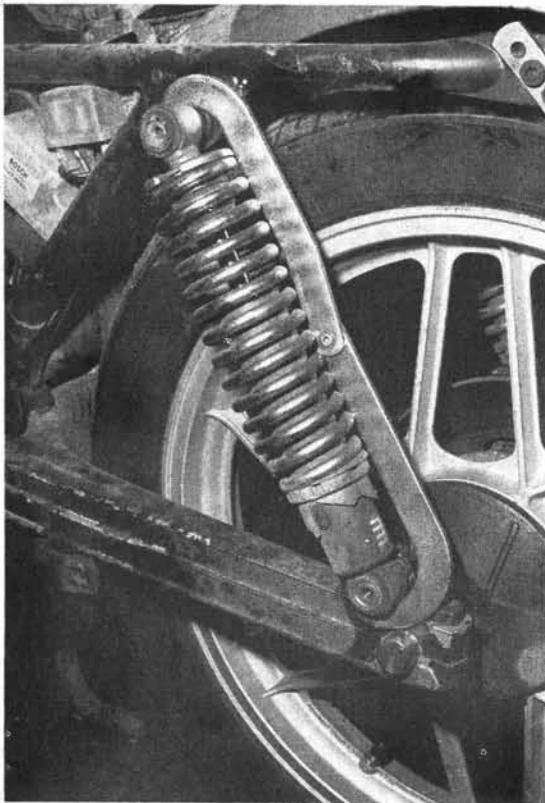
Outil de compression des ressorts de suspension arrière (Photo RMT)
